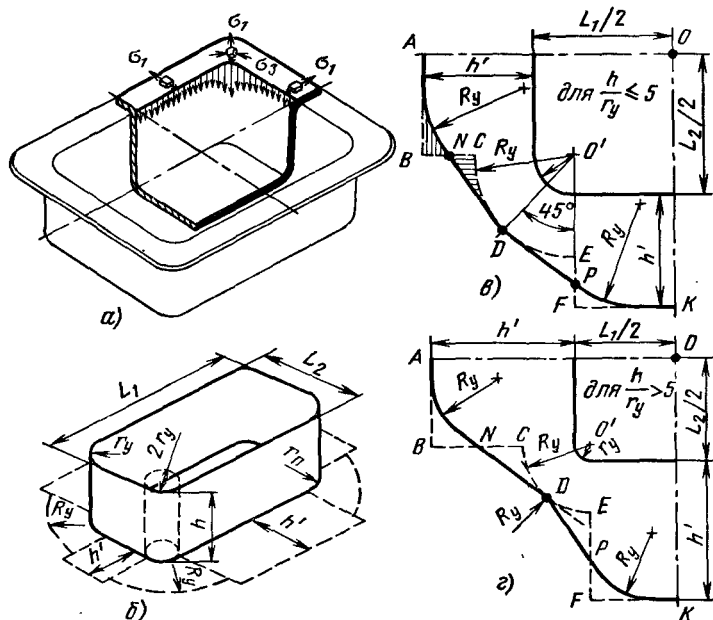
К построению контура заготовки для вытяжки полой коробчатой детали с прямоугольным дном (по Б. П. Звороно):
